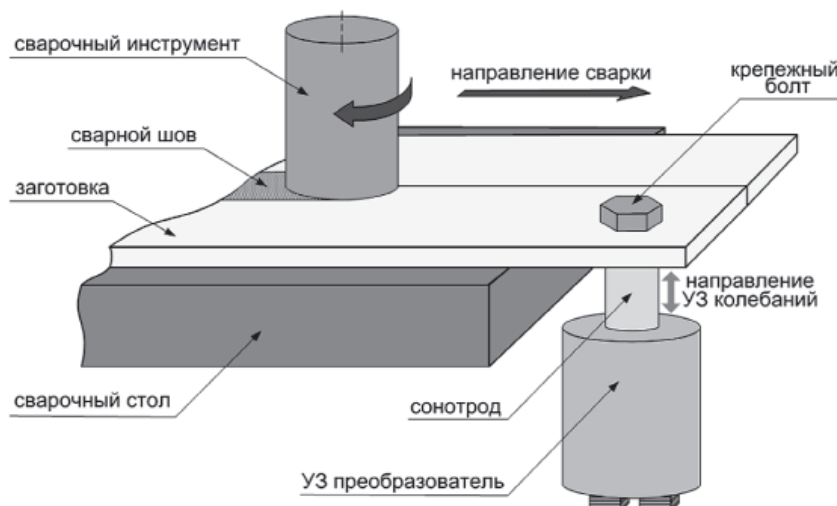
Схема сварки трением с перемешиванием с ультразвуковым воздействием
